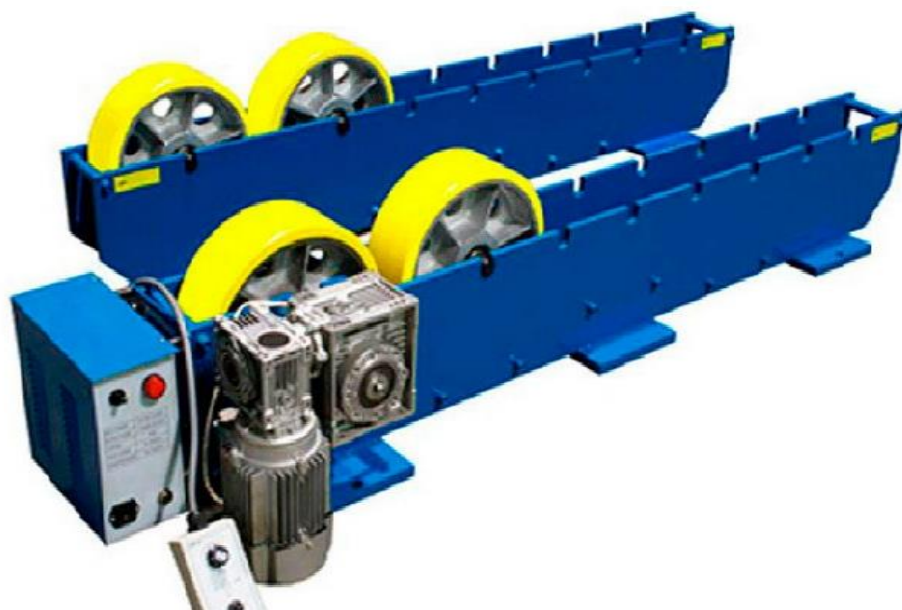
Роликовий зварювальний обертач NHTR-6000
